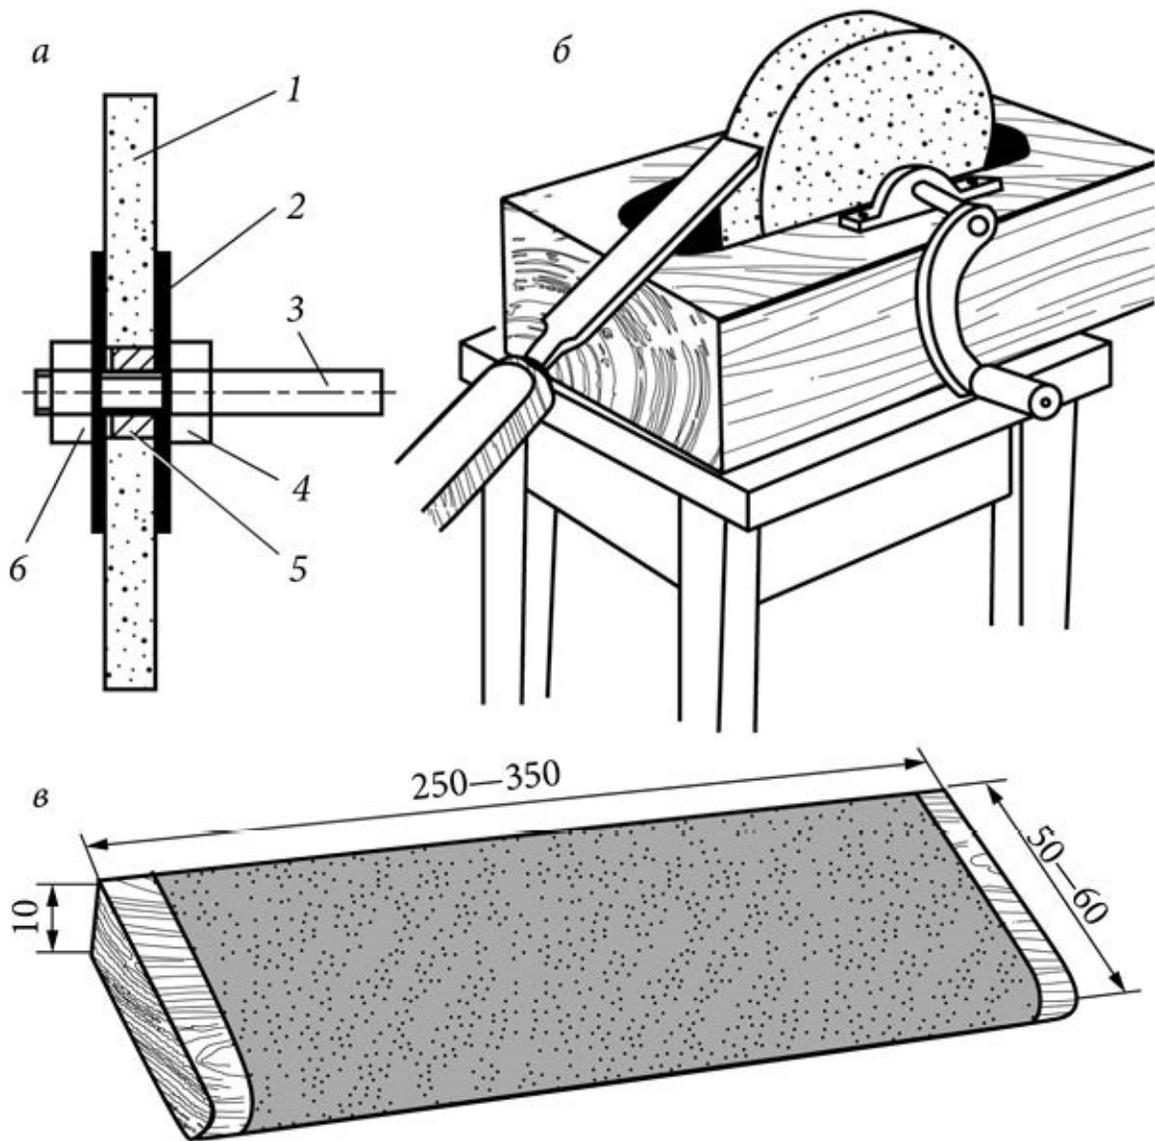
Оборудование для заточки и правки инструмента: а – абразивный точильный круг для ручной дрели в разрезе (1 – абразив; 2 – шайба; 3 – болт со срезанной головкой; 4 – гайка, навинченная до конца резьбы болта; 5 – вкладыш из металла или дерева; 6 – контргайка для сжатия пакета); б – водяное точило; в – заправочная доска.
